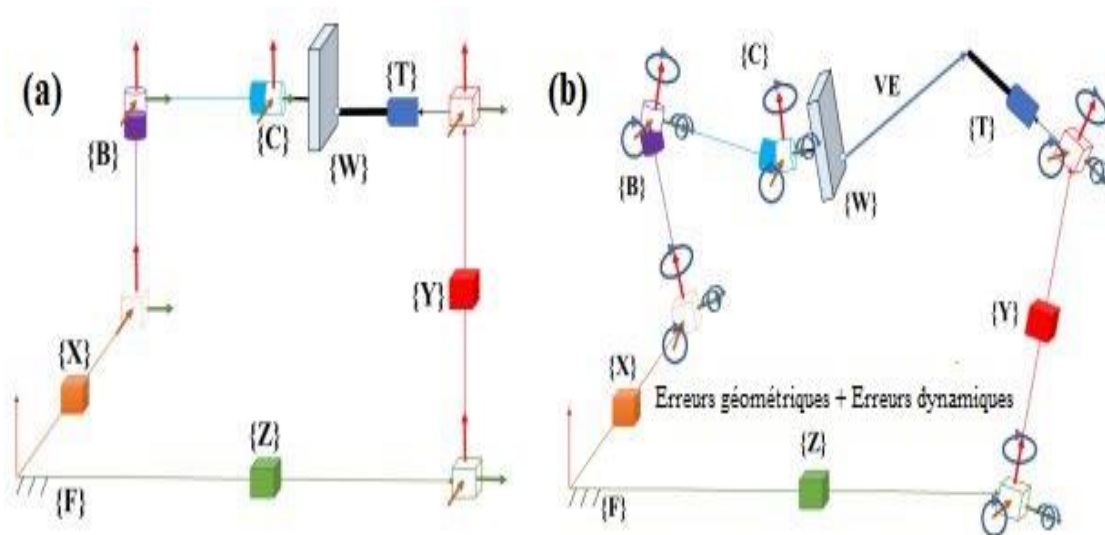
Erreurs volumétriques de la machine-outil, (a) Modèle d'erreur machine nominale de la machine-outil cinq axes HU40-T ; (b) Modèle d'erreur machine réelle contenant les erreurs géométriques et les erreurs dynamiques [19].
